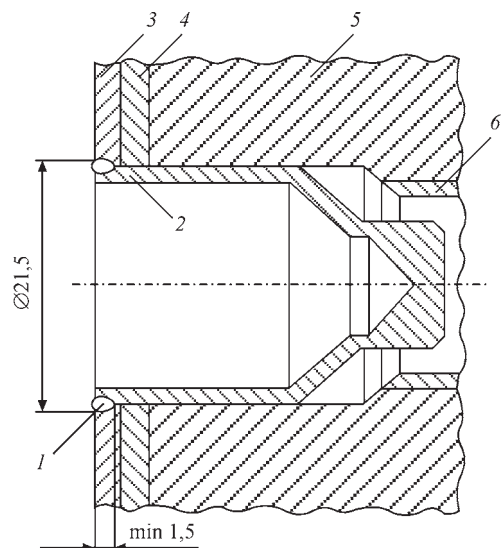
Схема вварювання заглушки: 1 — шов; 2 — заглушка; 3 — перший шар наплавлення; 4 — другий шар наплавлення; 5 — стінка ПГ; 6 — ТОТ
